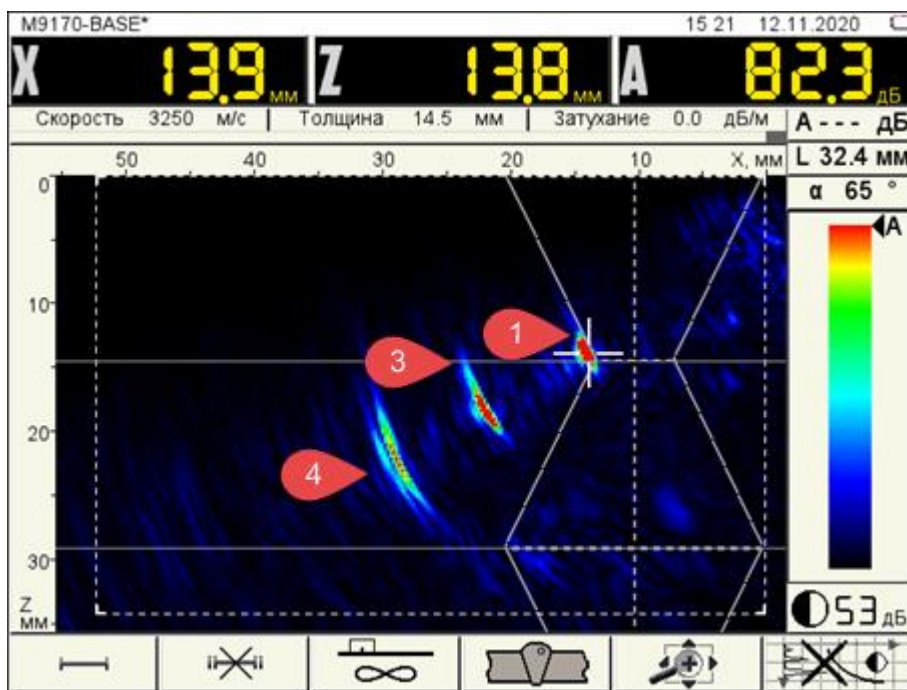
Образы ложных отражателей на сварном шве. Положение 2.
